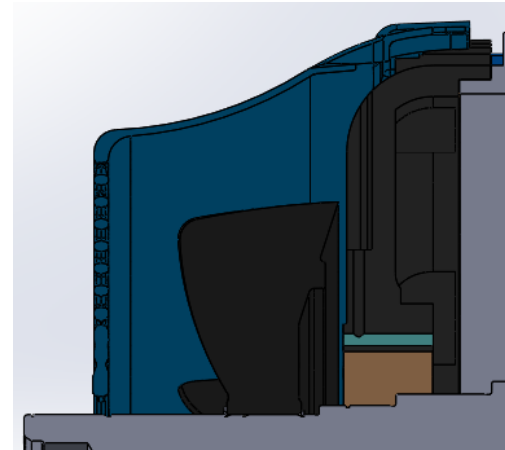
Posição 1 (Ventilador 420x134, Cota P = 31 mm, Cota H = 6 mm, Cota F = 58.24 mm)
